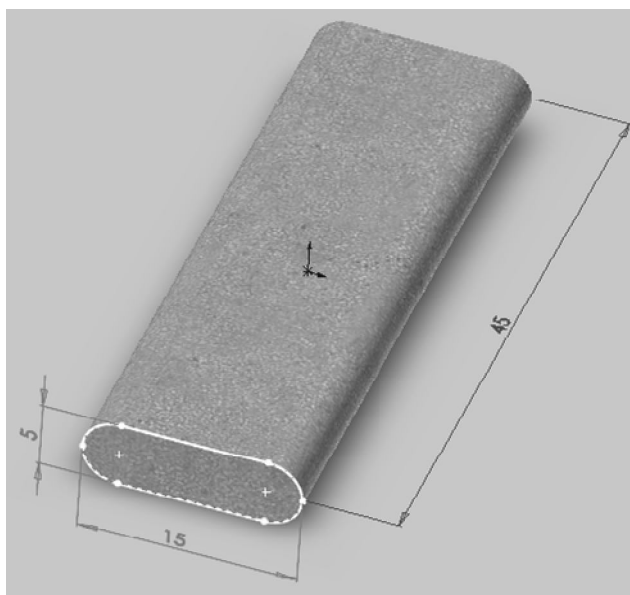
Dimensões em mm do arame da armadura de tração cortado.
